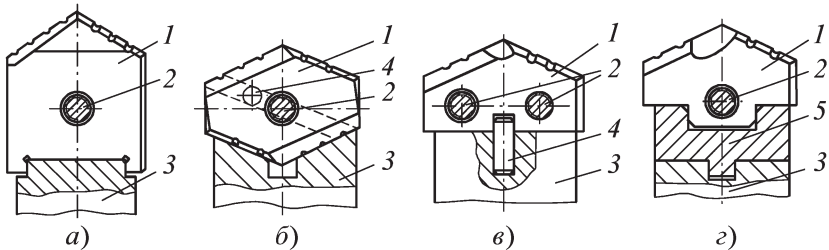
Сборное перовое сверло для сверления глубоких отверстий:
